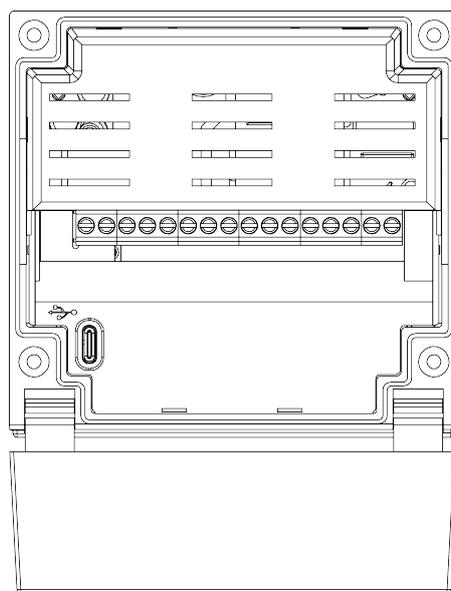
Расположение разъема USB для корпуса Н
